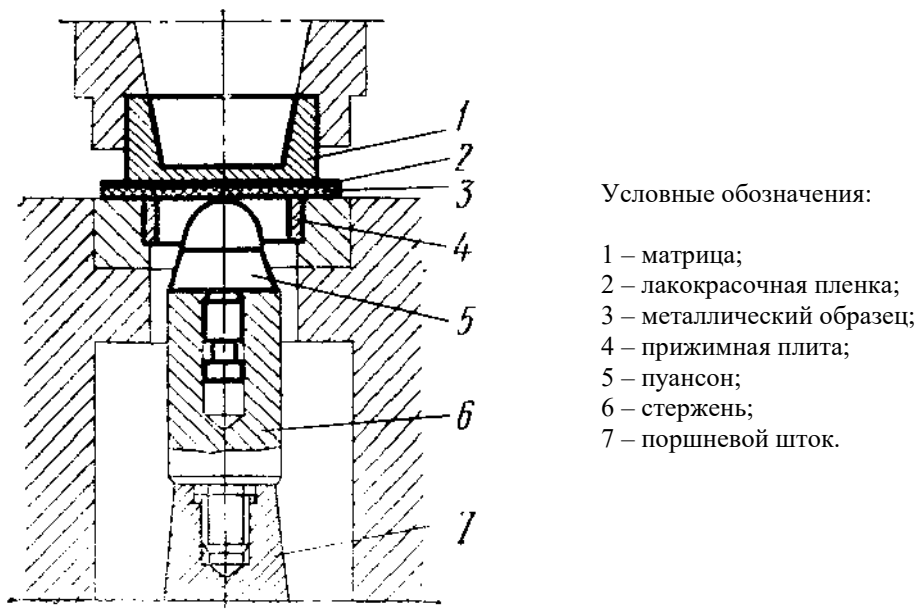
Схема рабочей части прибора «Пресс Эриксона»
